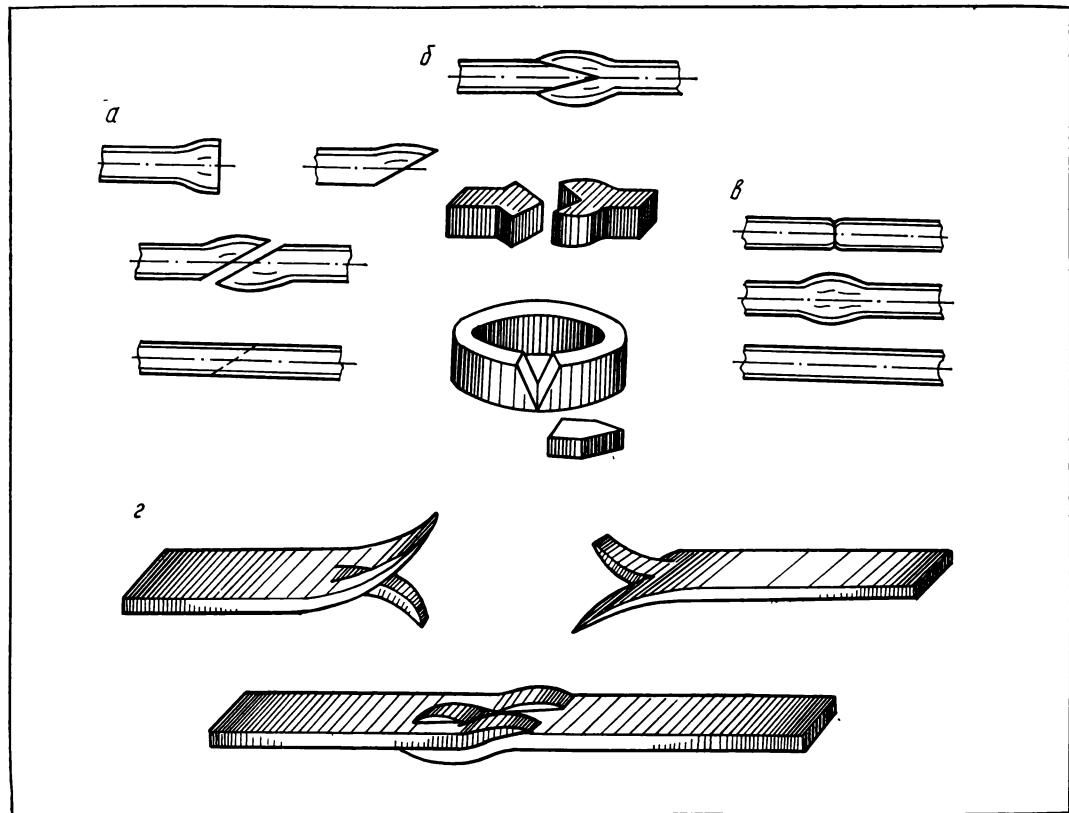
Приемы подготовки концов деталей при кузнецкой сварке:
